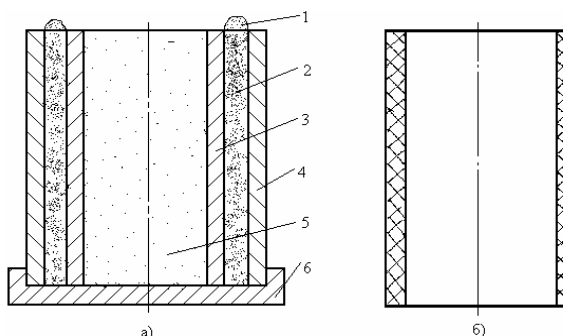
Цилиндрическая конфигурация пресс-формы: а) форма в сборе; б) фильтрующий элемент; 1) термит; 2) порошкообразная шихта; 3) внутренняя вставка; 4) металлическая форма; 5) засыпка внутренней полости; 6) дно
